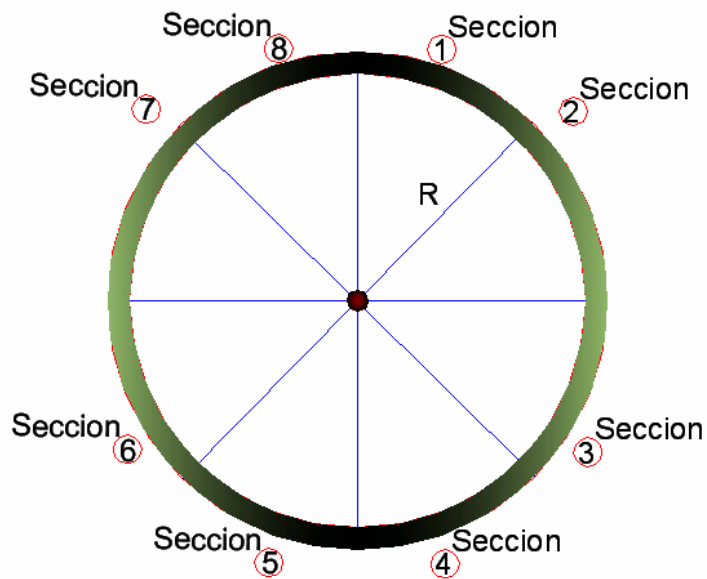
Seccionamiento de tuberías 160 mm a 315 mm
